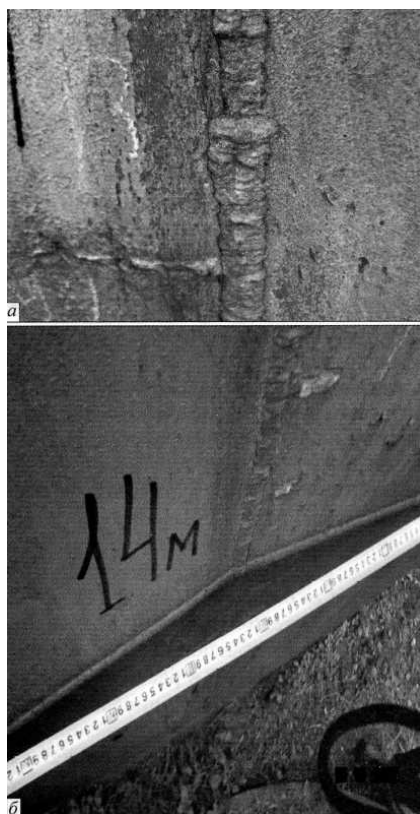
РВС 10 тыс. м³: усталостные трещины по зоне сплавления шва (а); угловые деформации в вертикальном стыковом монтажном сварном соединении стенки (б)
